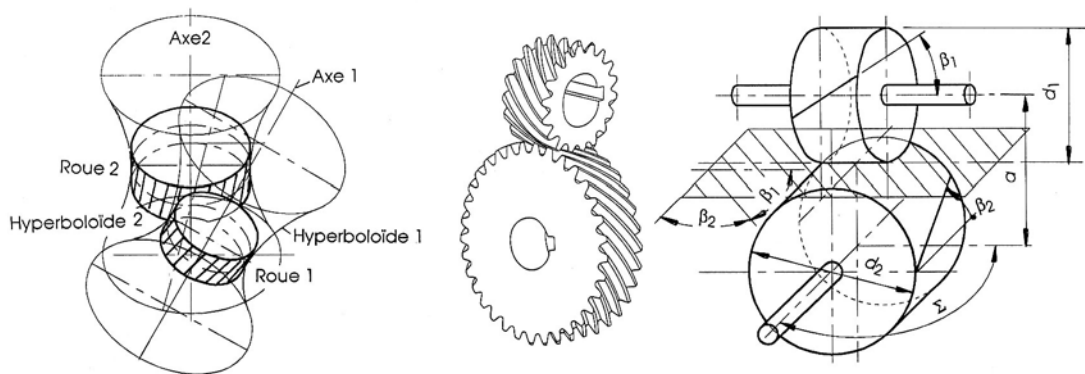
Géométrie des hyperboloïdes pour engrenages à axes gauches, engrenage gauche
